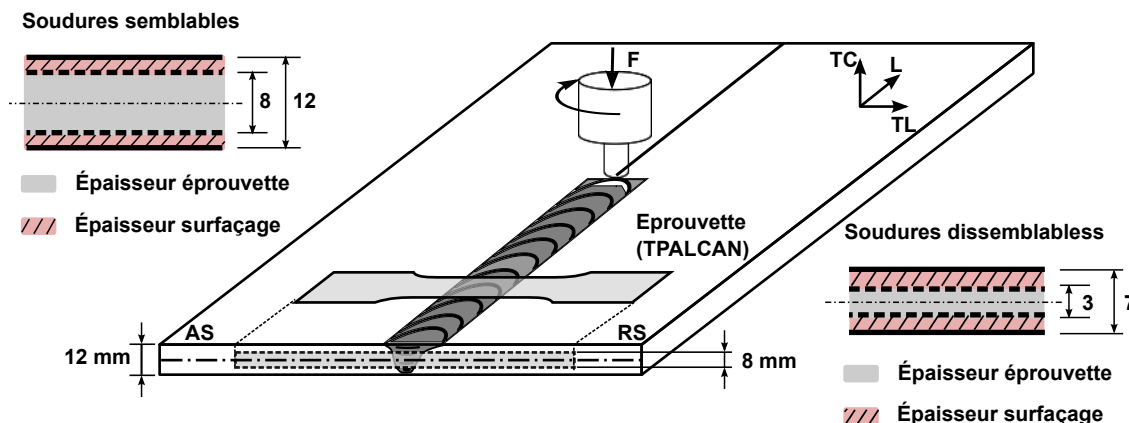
Schéma de prélèvement des éprouvettes de traction monotone et de fatigue dans les plaques soudées par FSW
